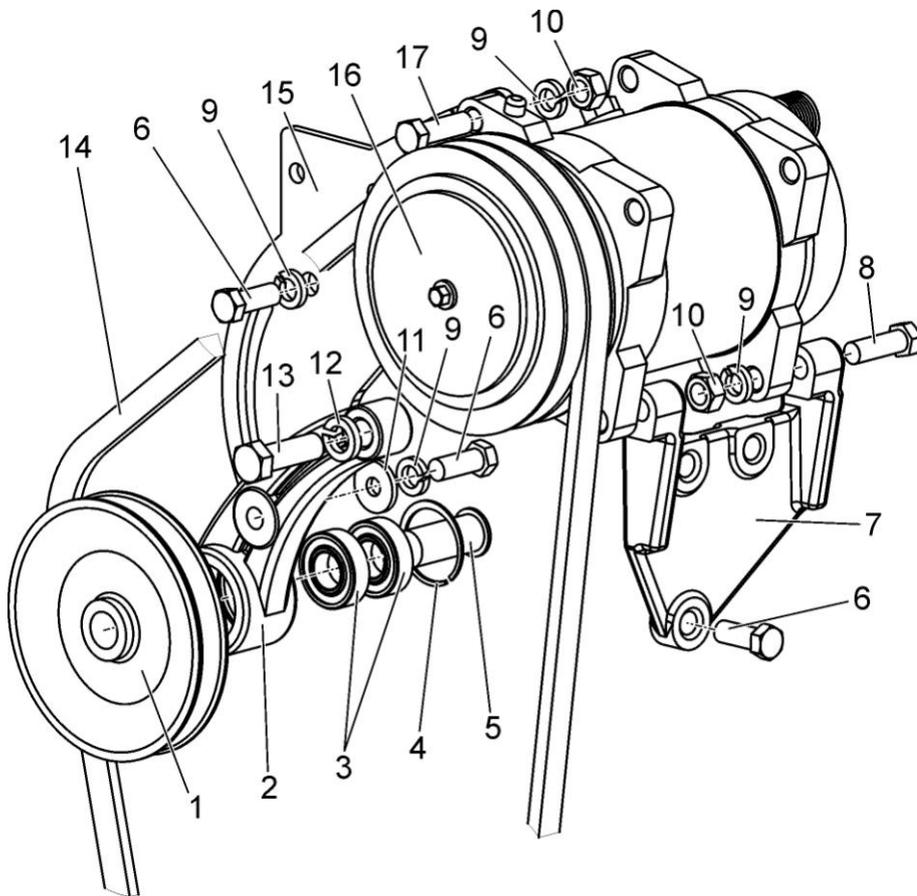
Компрессор кондиционера с приводом. Рычаг натяжной
